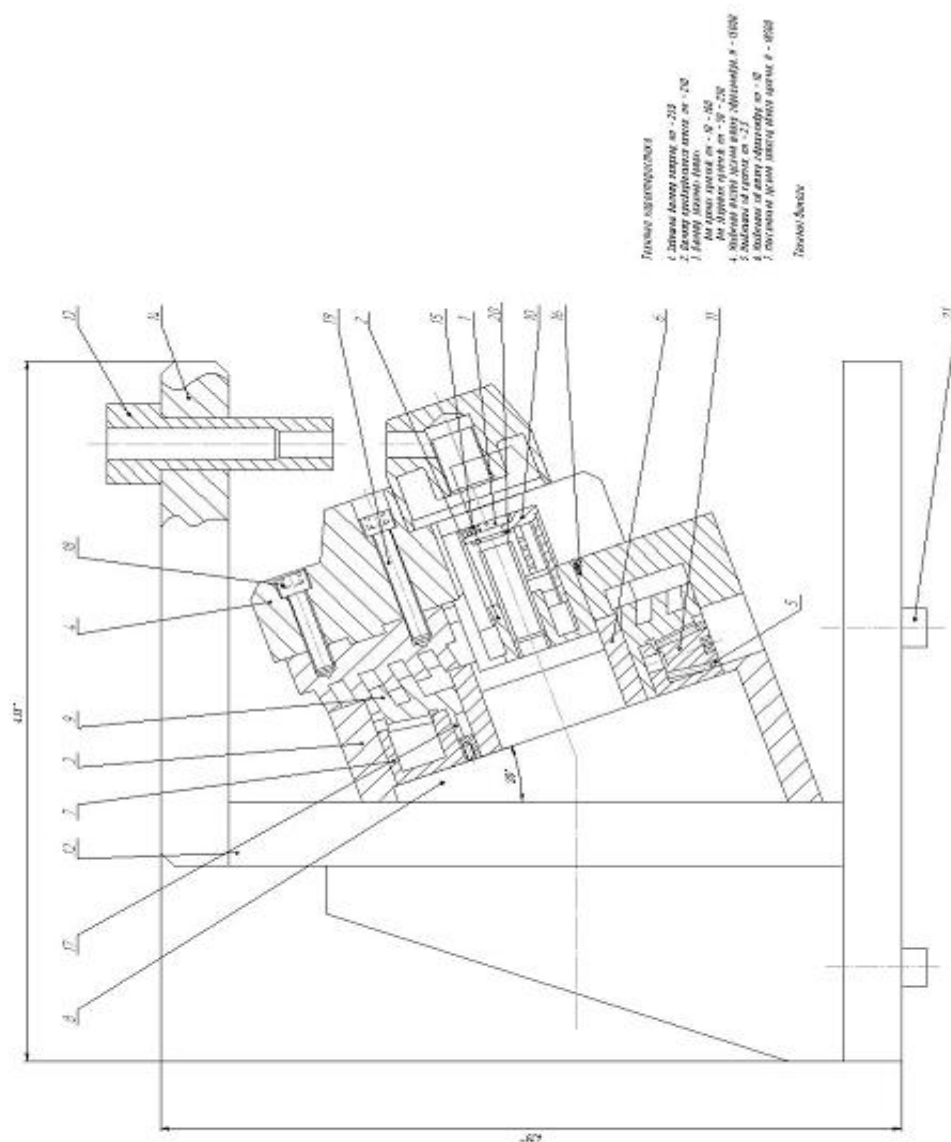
Самоцентруючий патрон 3-х кулачковий з пневмоприводом для свердлення отворів на верстаті з ЧПК
